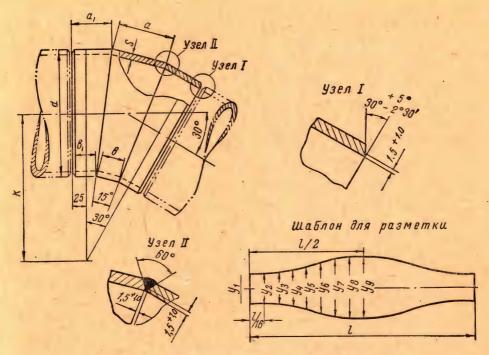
Отвод сварной с углом поворота 30°.
